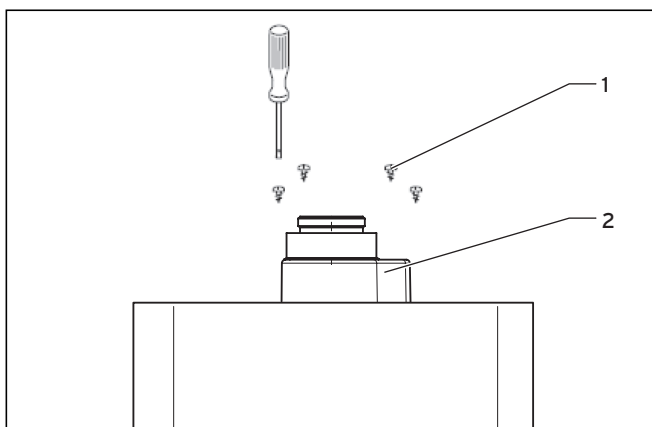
Desmontaje de la pieza de empalme del aparato
